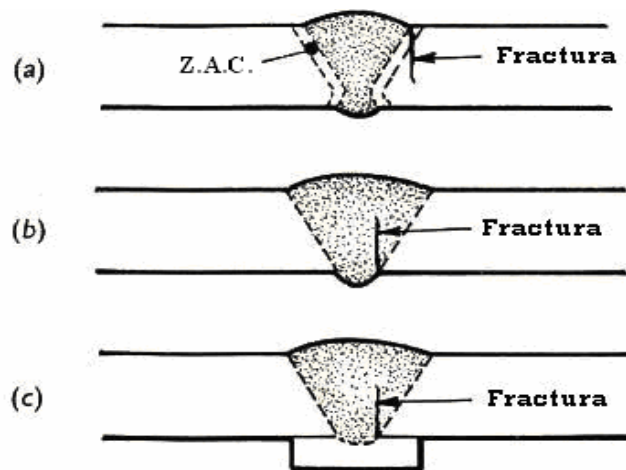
Modos típicos de fractura en especímenes de soldadura a tope⁽¹⁵⁾. ZAC: Zona Afectada por el Calor.
